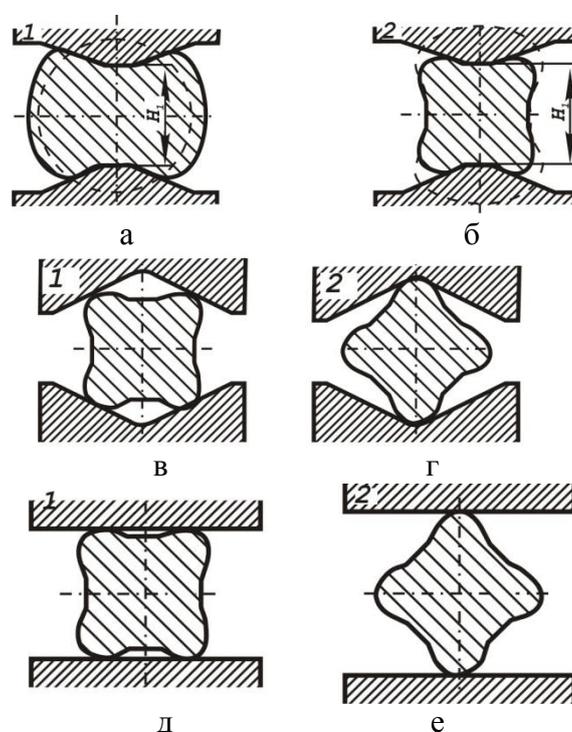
Последовательность получения четырехлучевой заготовки (а, б) и схемы обкатки четырехлучевой заготовки на круглое сечение вырезными (в, г) и плоскими бойками (д, е)
